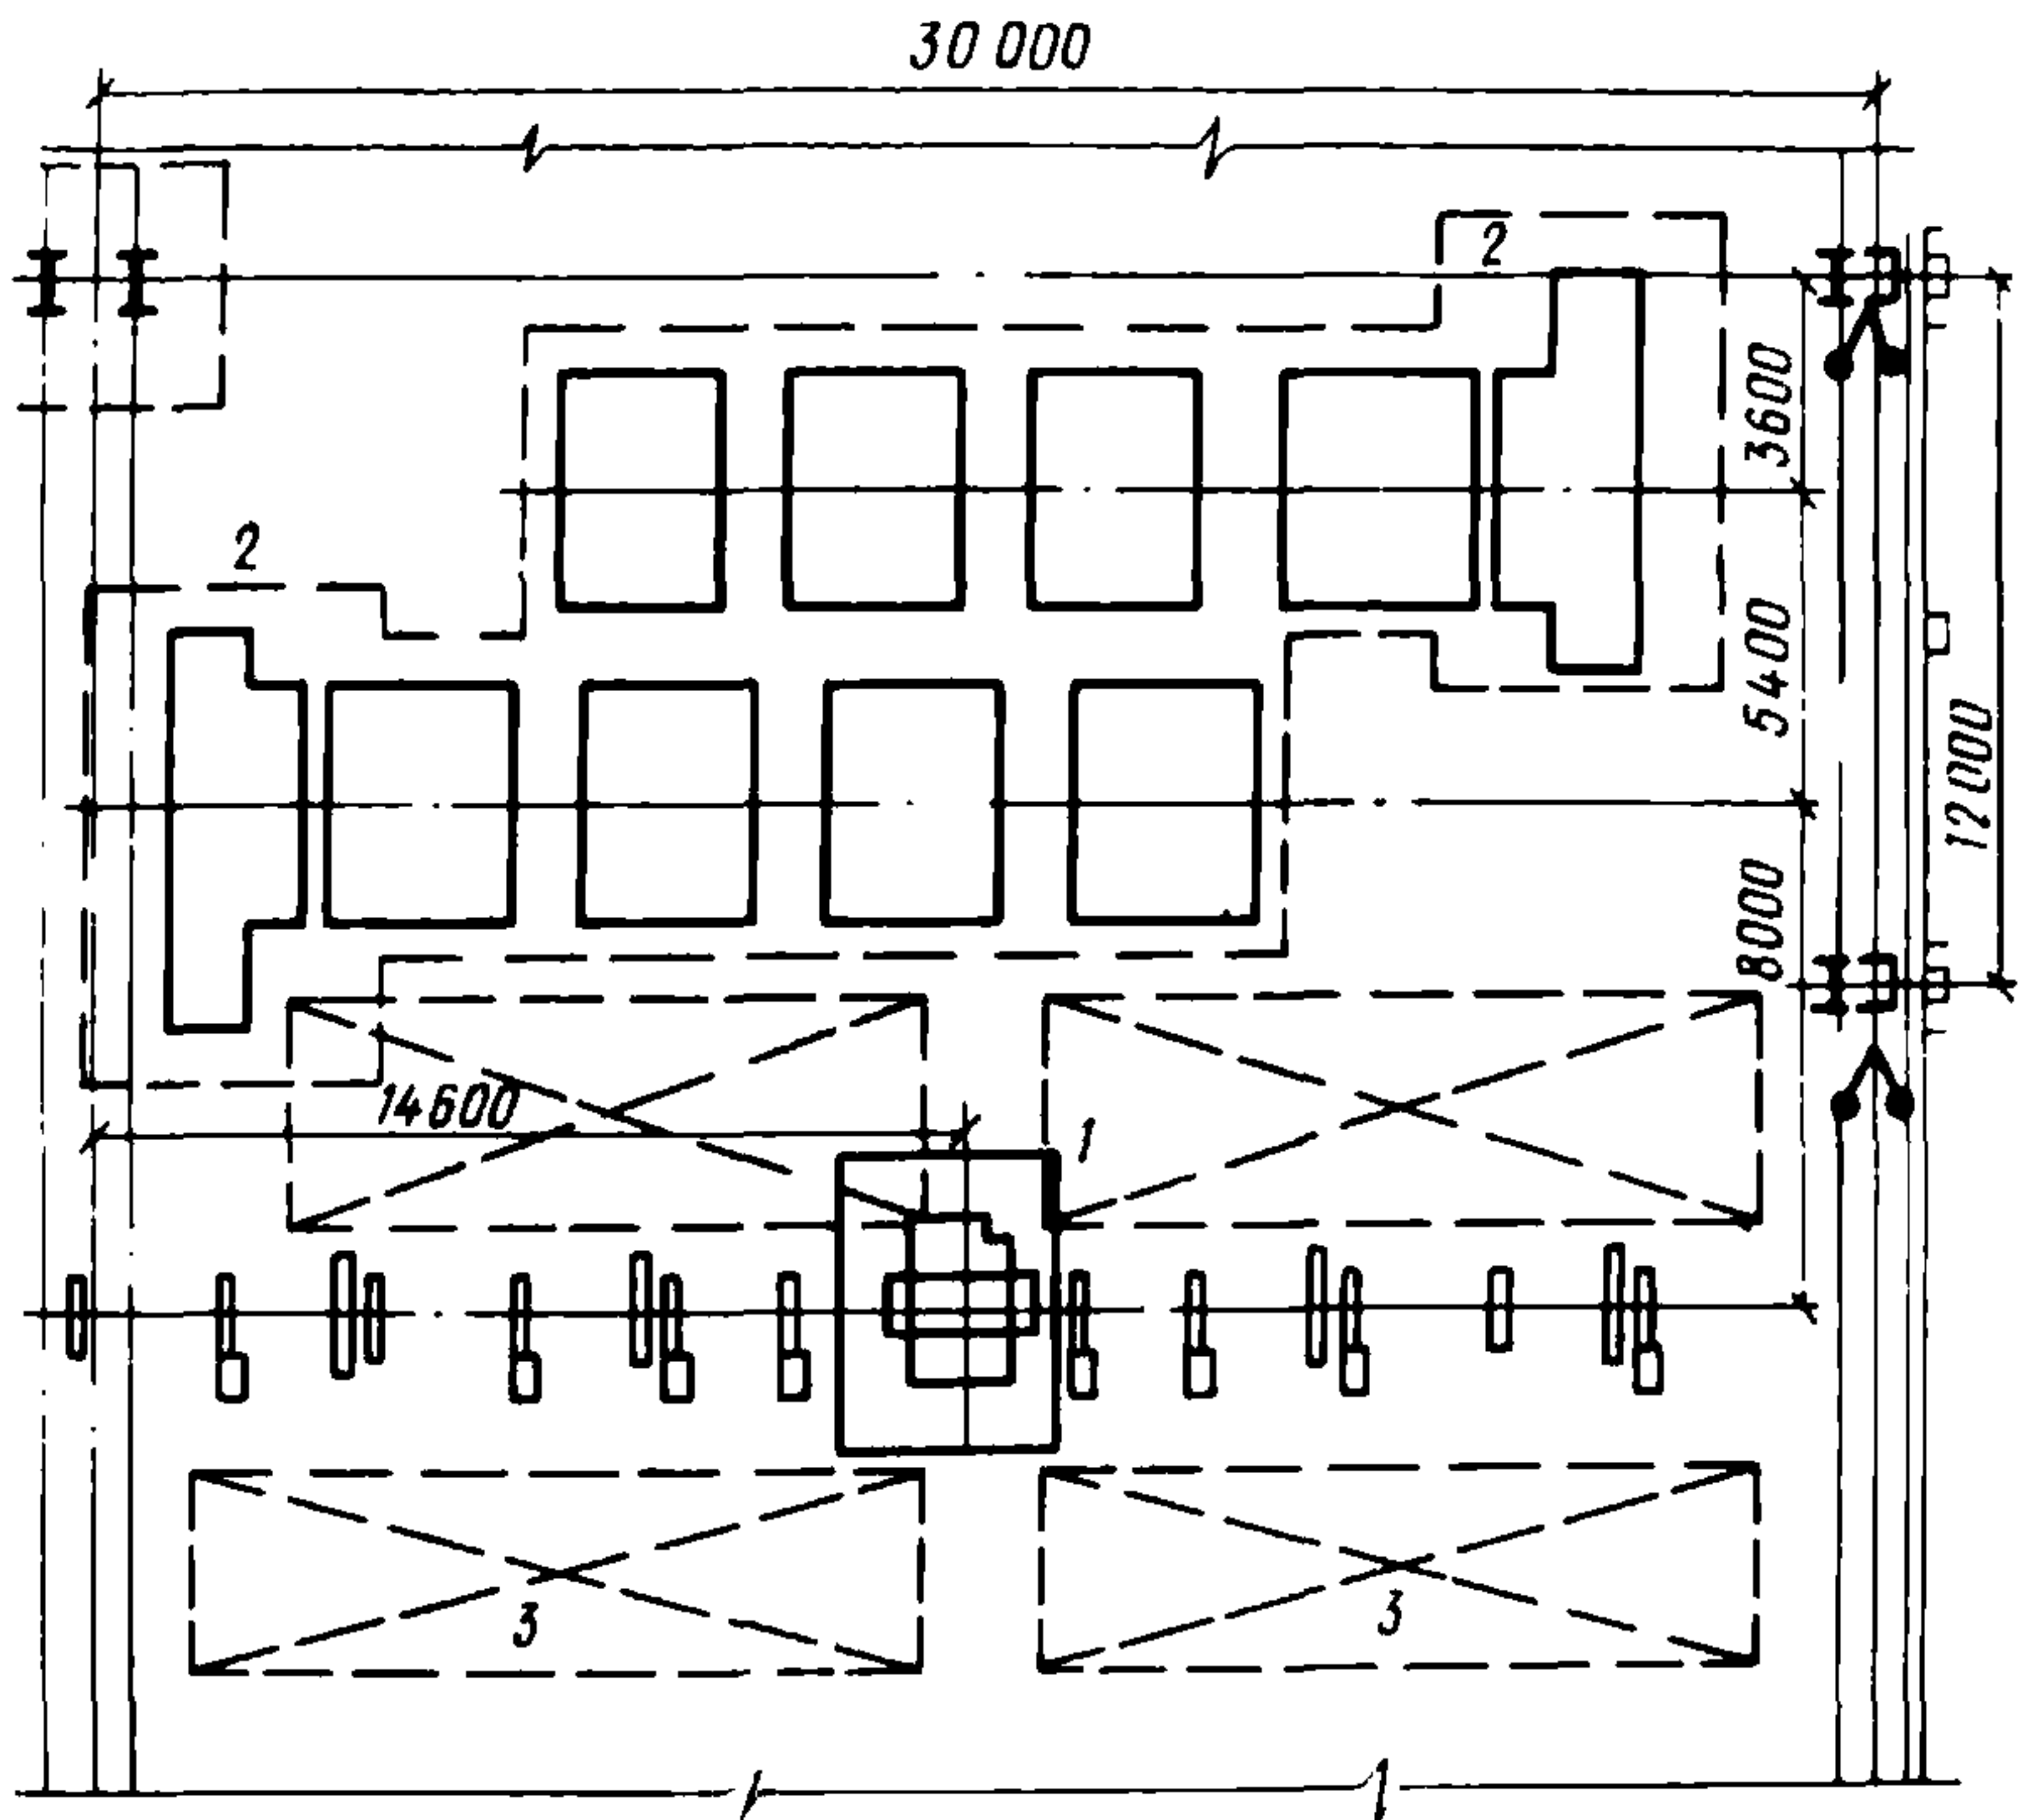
Планировка участка правки и фрезеровки стержней двутаврового сечения
